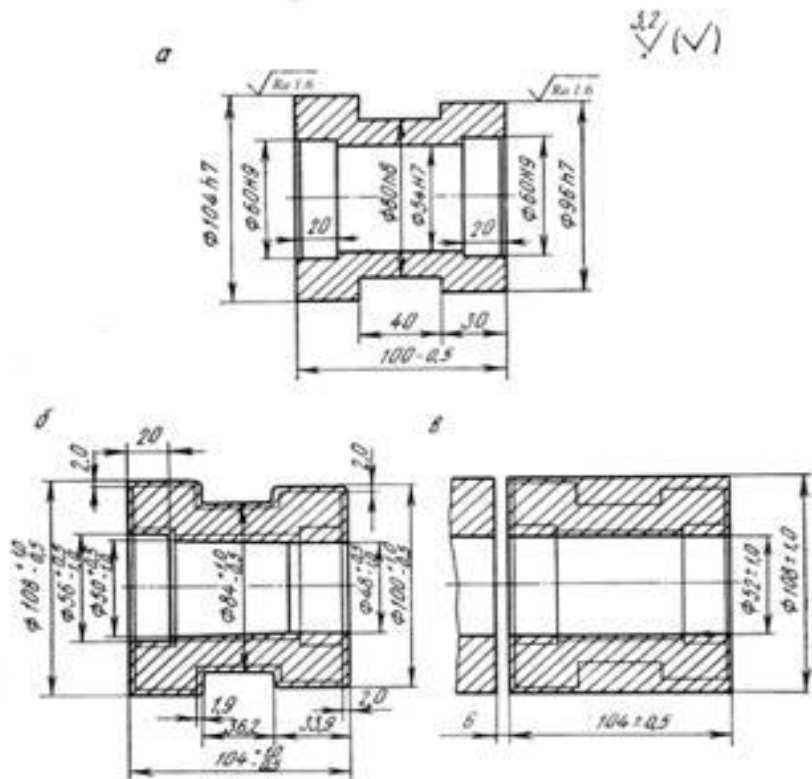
Втулка: а – оброблена деталь; б – штамповка на ГKM; в – заготовка із труби.
